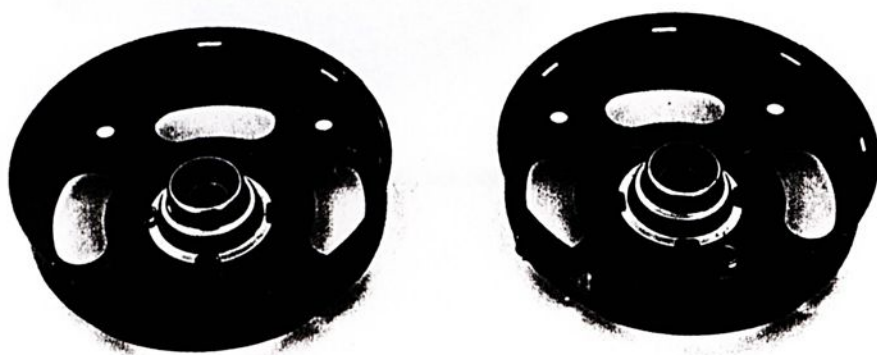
TAMPAS TRASEIRAS DO CONJUNTO ROTOR - ESTATOR
